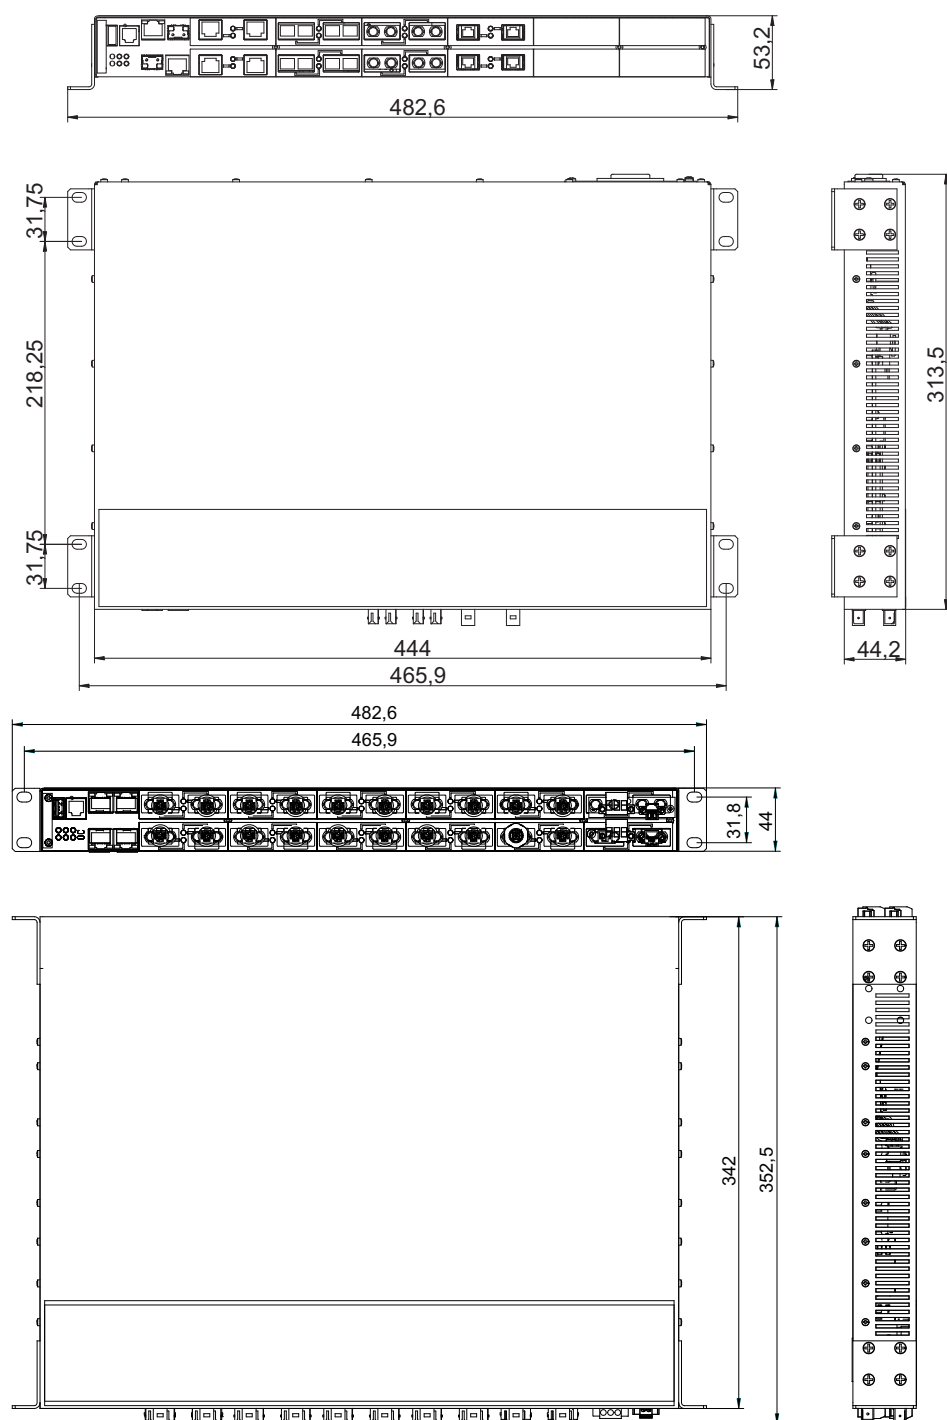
MACH1000, Abmessungen der Gerätevarianten
